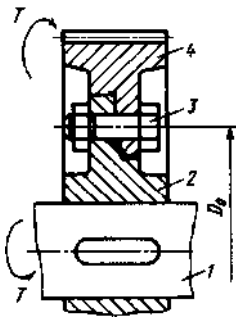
Болтовое соединение венца зубчатого колеса с центром:
